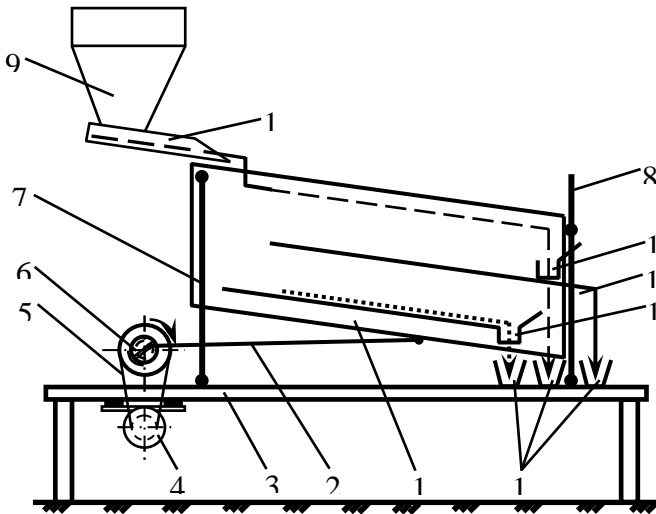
Конструктивно-технологічна схема установки для калібрування: 1 – решітна частина; 2 – шатун; 3 – рама; 4 – електродвигун; 5 – пасова передача; 6 – вал із регулюванням амплітуди коливань; 7 – передні стояки; 8 – задні стояки з механізмом регулювання кута нахилу решіт; 9 – бункер для насіння; 10 – розподільна скатна дошка; 11, 12, 13 лотки для виведення фракцій; 14 – приймальні лотки
